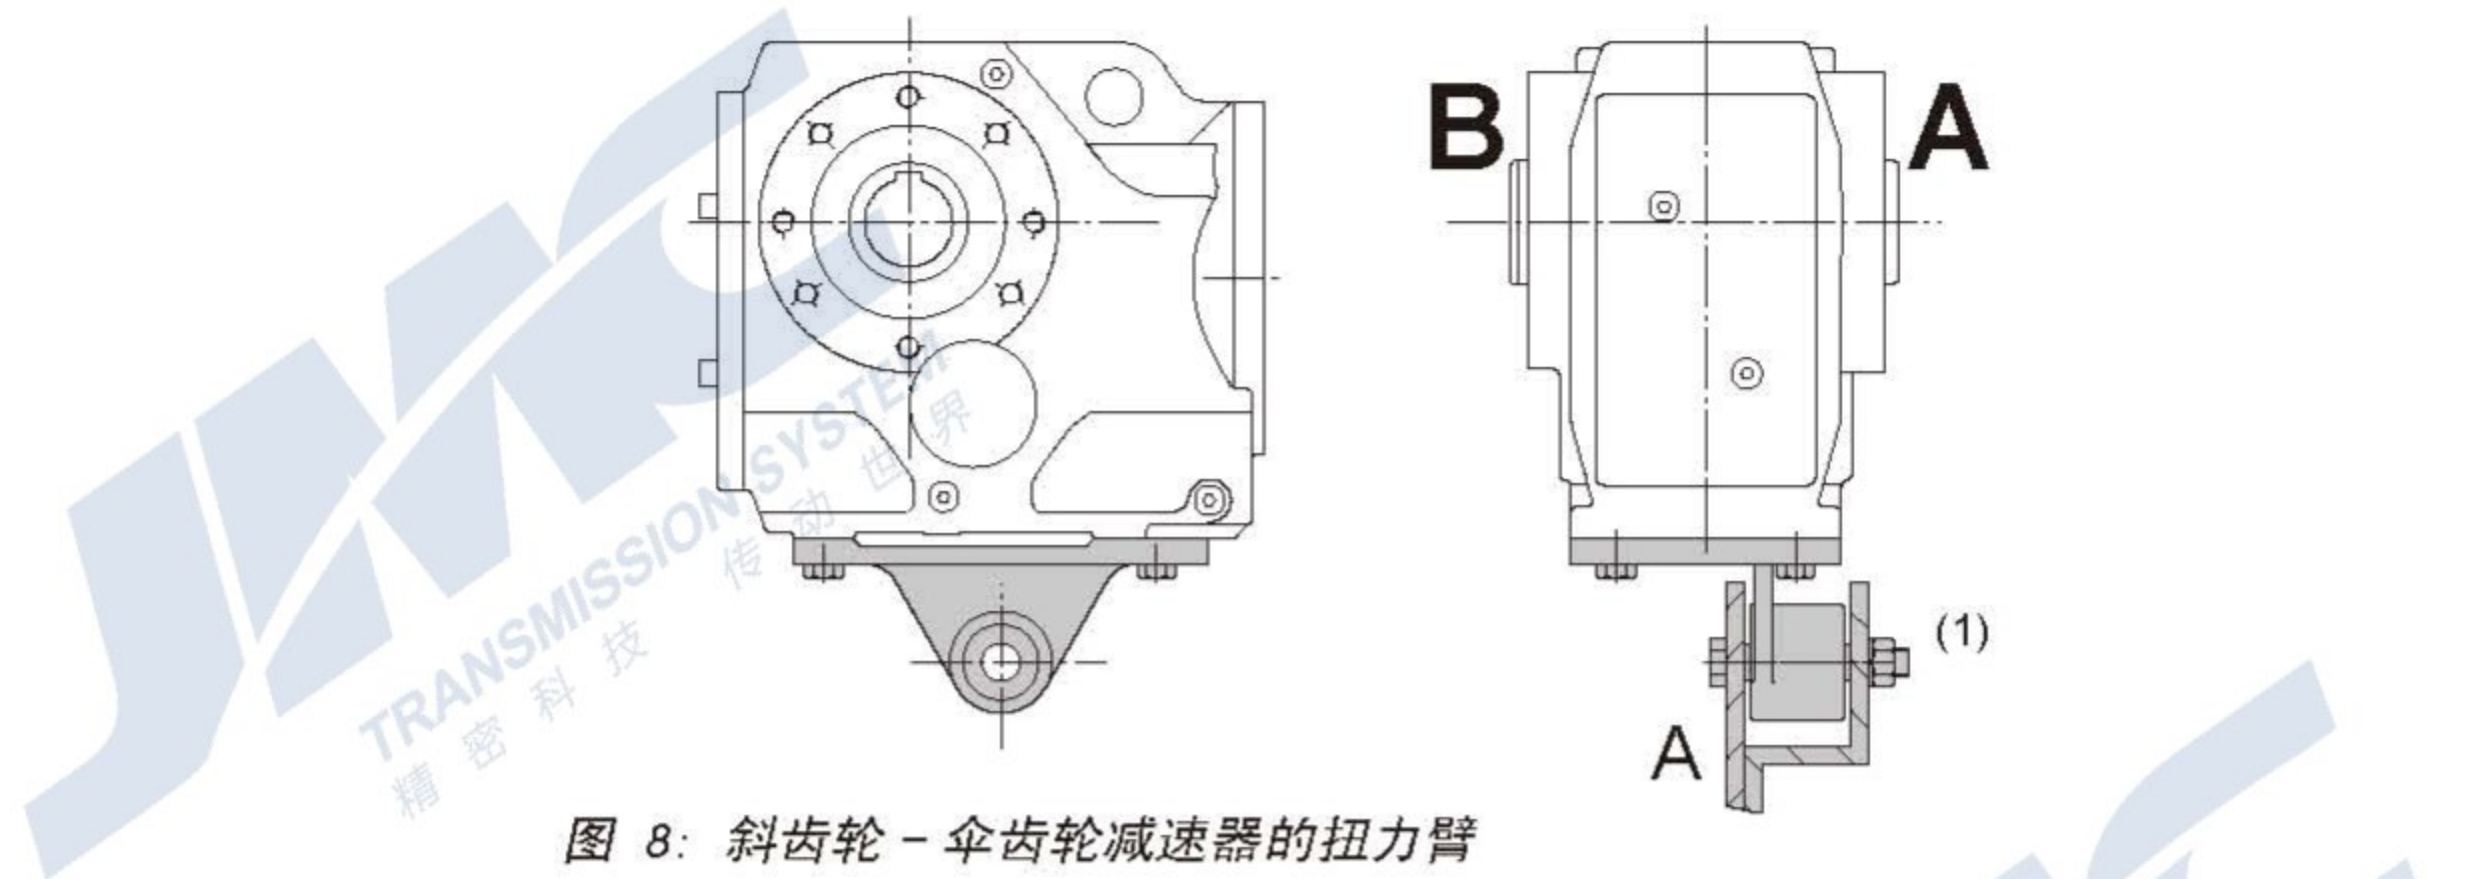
斜齿轮 - 伞齿轮减速器的扭力臂
